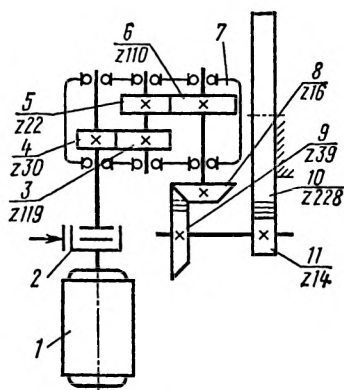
Кинематическая схема механизма поворота крана ДЭК-251:
